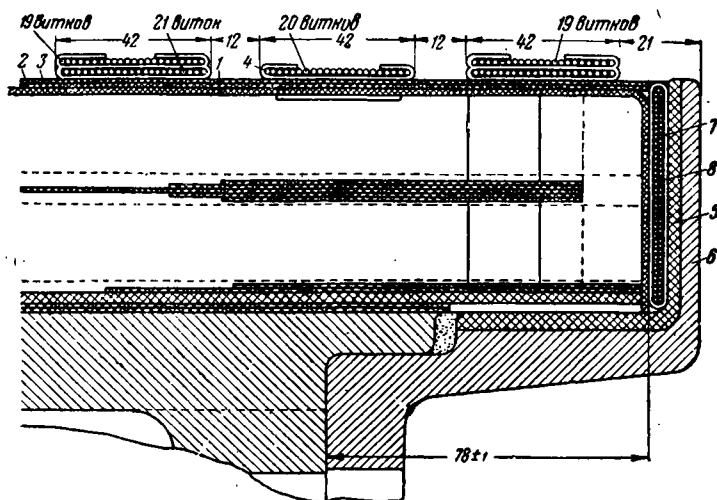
Разрез задней лобовой части обмотки якоря тягового двигателя ДПЭ-400:
